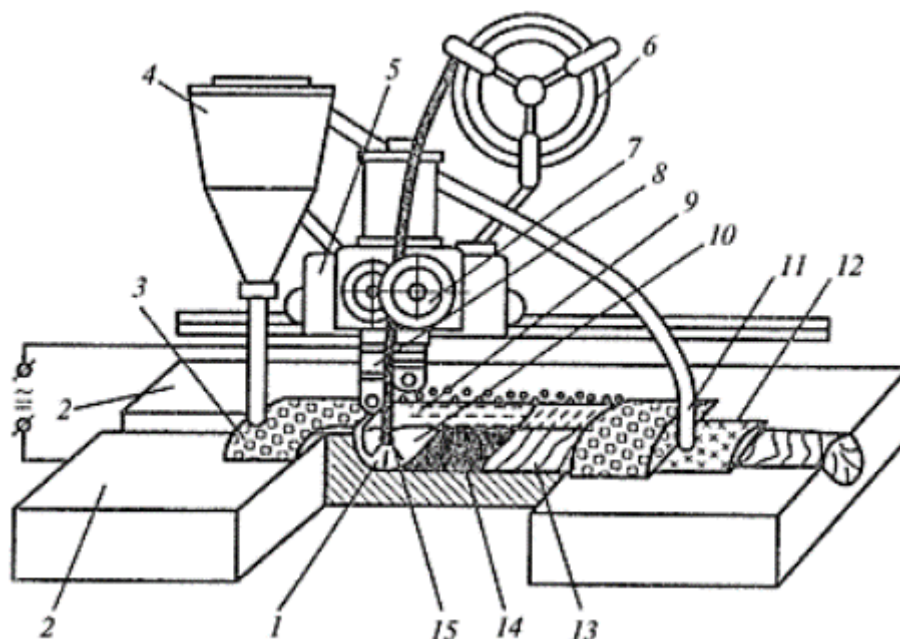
Схема автоматической сварки пол флюсом [11]:
